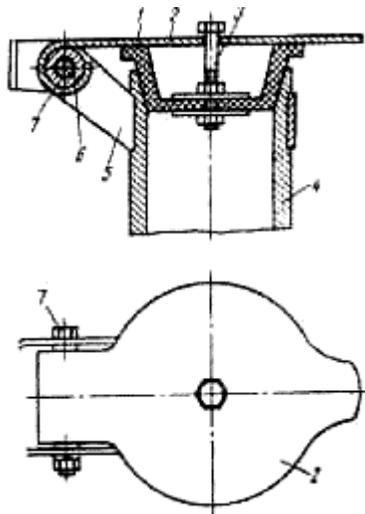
Штуцер-клапан: 1 — резиновая конусная пробка; 2 — крышка; 3 — болт крепления пробки; 4 — корпус; 5 — хомут; 6 — втулка, ограничивающая откидывание крышки; 7 — болт-ось.
